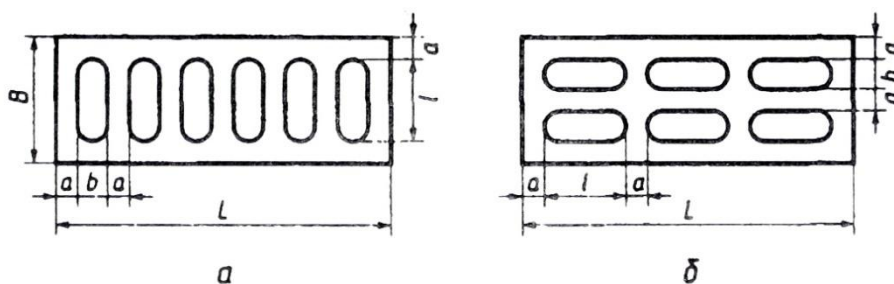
Схемы расположения тестовых заготовок на люльке печи:
